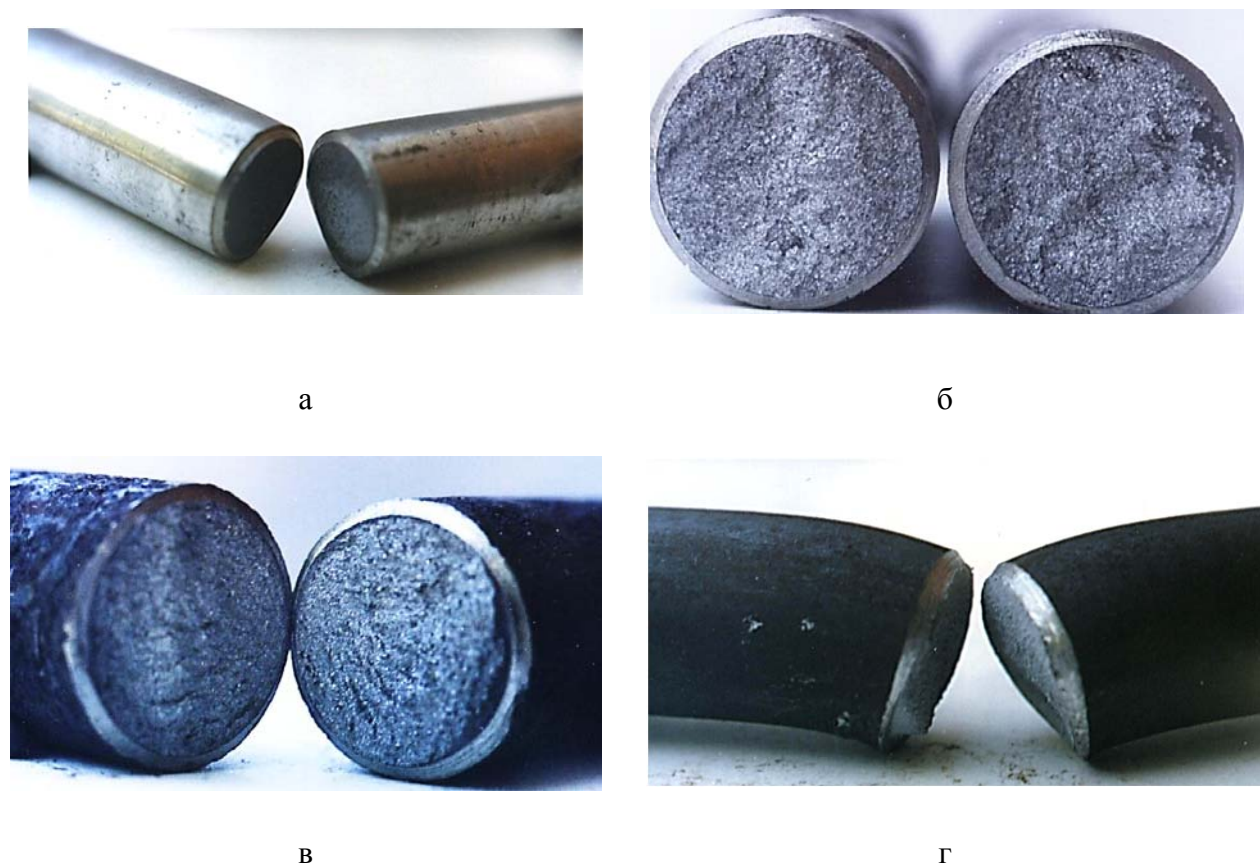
Заготовки из стали (а – Сталь 50ХФА; б – Сталь 30; в – Сталь 40; г – Ст. 3), полученные способом трёхточечной холодной ломки изгибом при статико-динамическом нагружении
